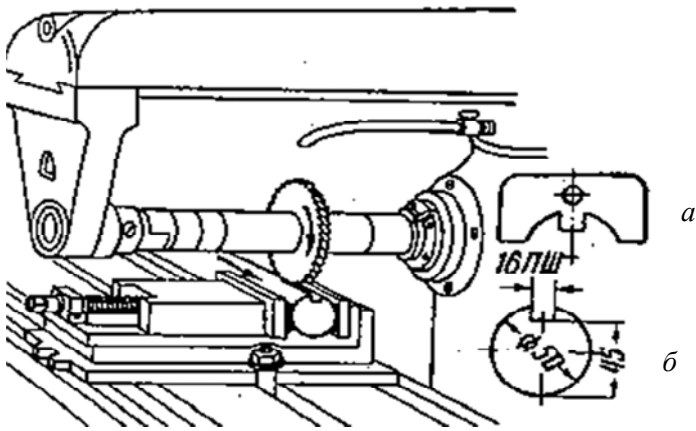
Фрезерование дисковой фрезой открытой шпоночной канавки на валу
